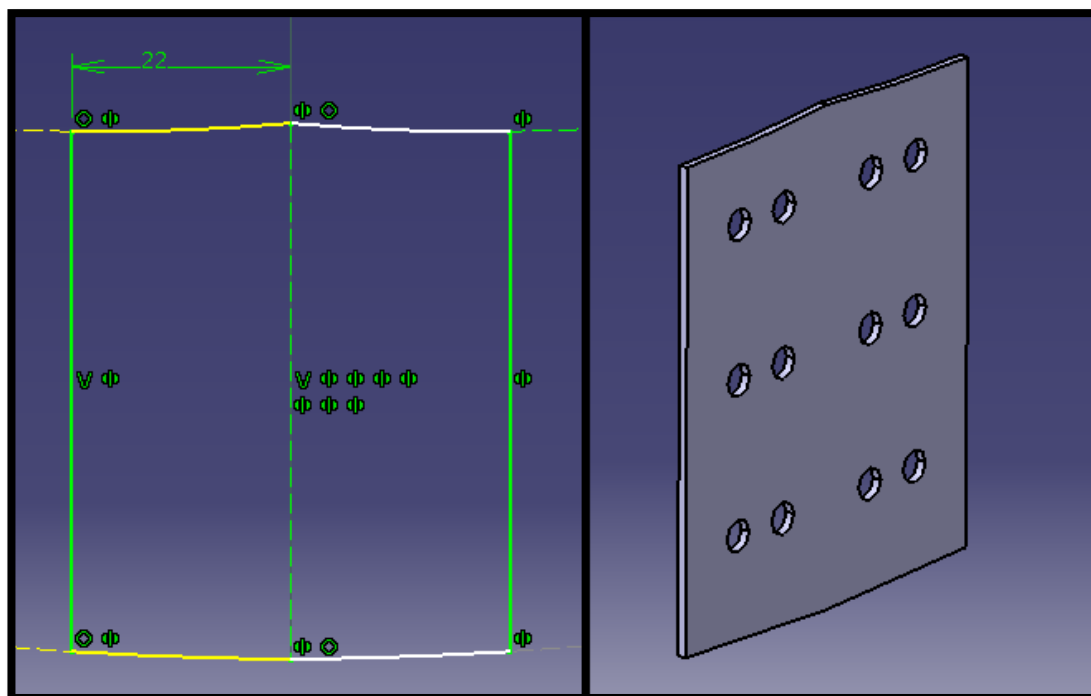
Refuerzo inferior 13: Sketch y pieza final tras extrusión y vaciado
